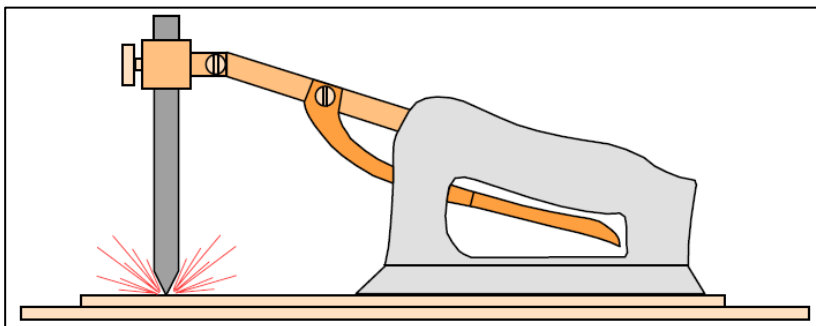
Método de soldagem segundo a patente de Bernardos.
